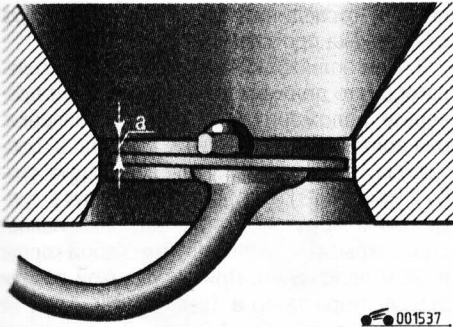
Измеритель потока воздуха: а – контрольный размер
